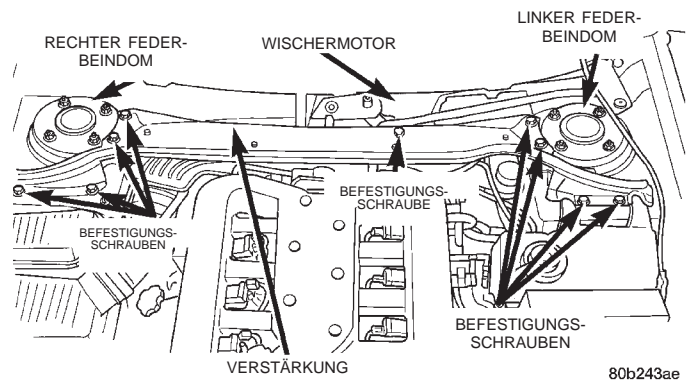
Befestigung der Verstärkung am Fahrzeug
